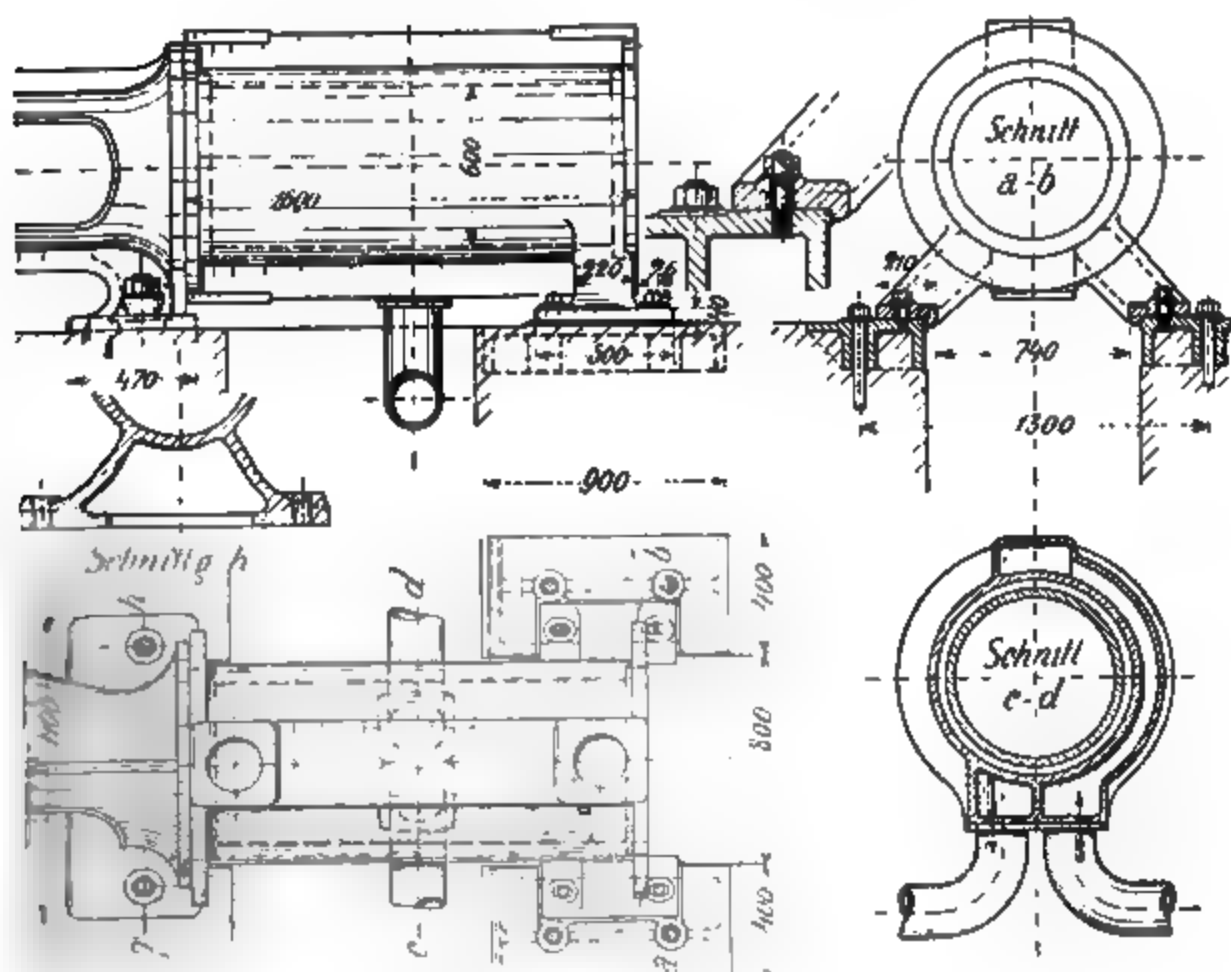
1265. Dampfeylinder für Maschine 600 × 1050.
